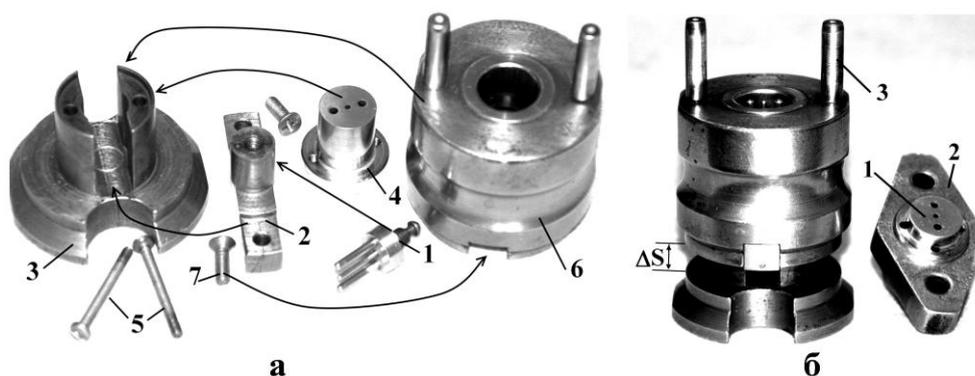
Конструкция штампа с плавающей матрицей.
